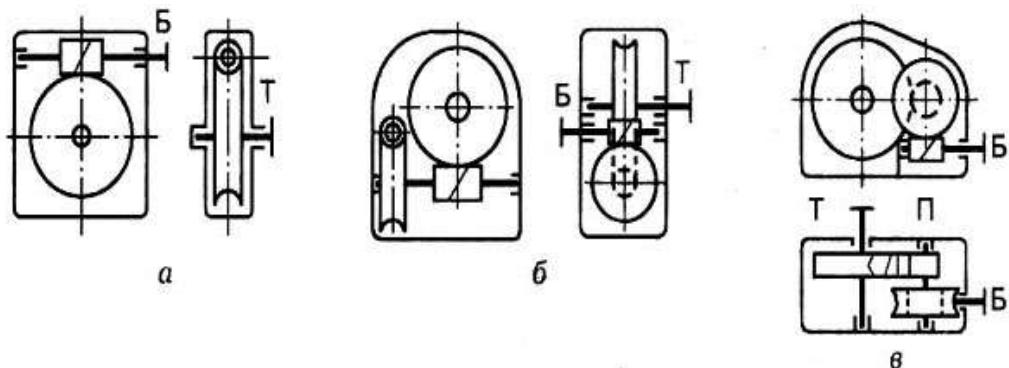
Схемы червячных редукторов: а — одноступенчатый; б — двухступенчатый;
